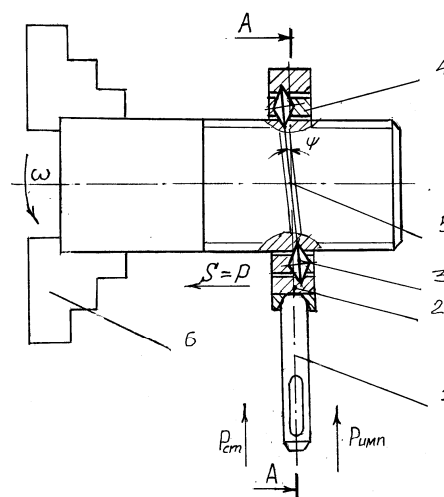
Охватывающий инструмент с роликами в сепараторе для статико-импульсного отделочно-упрочняющего накатывания резьбы:
